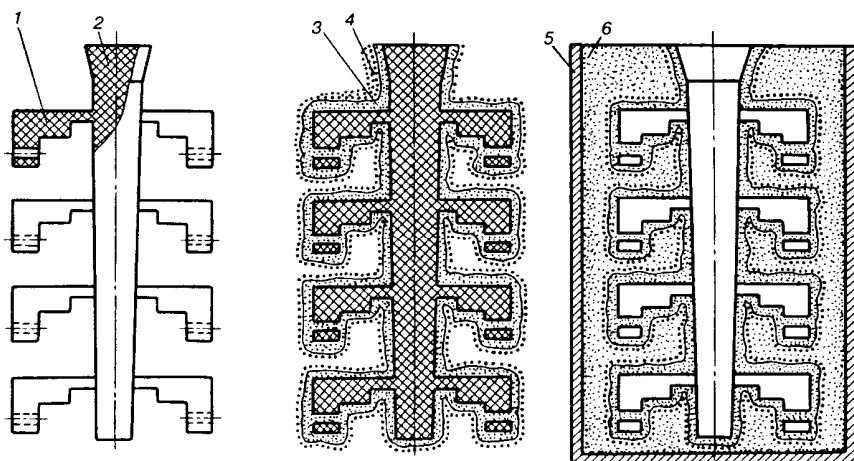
Схема виготовлення форми за виплавлюваними моделями
